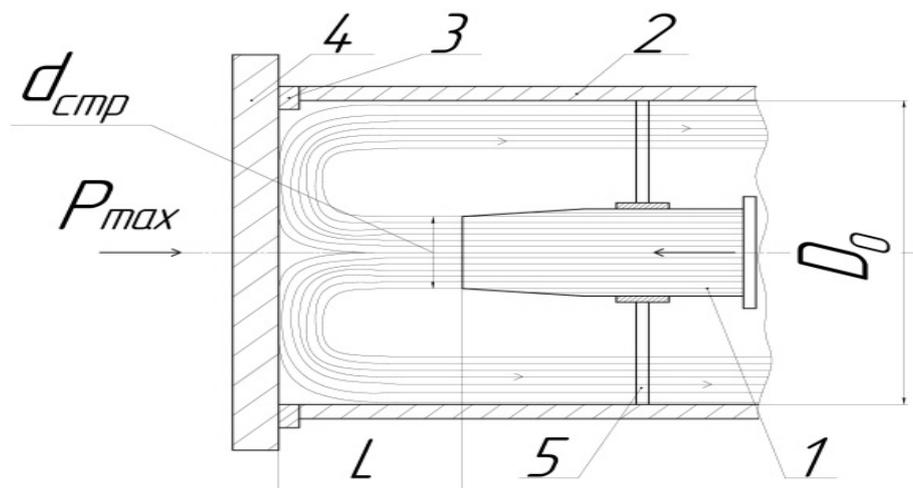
Схема струйного устройства для реализации процесса реверсивно-струйной очистки
